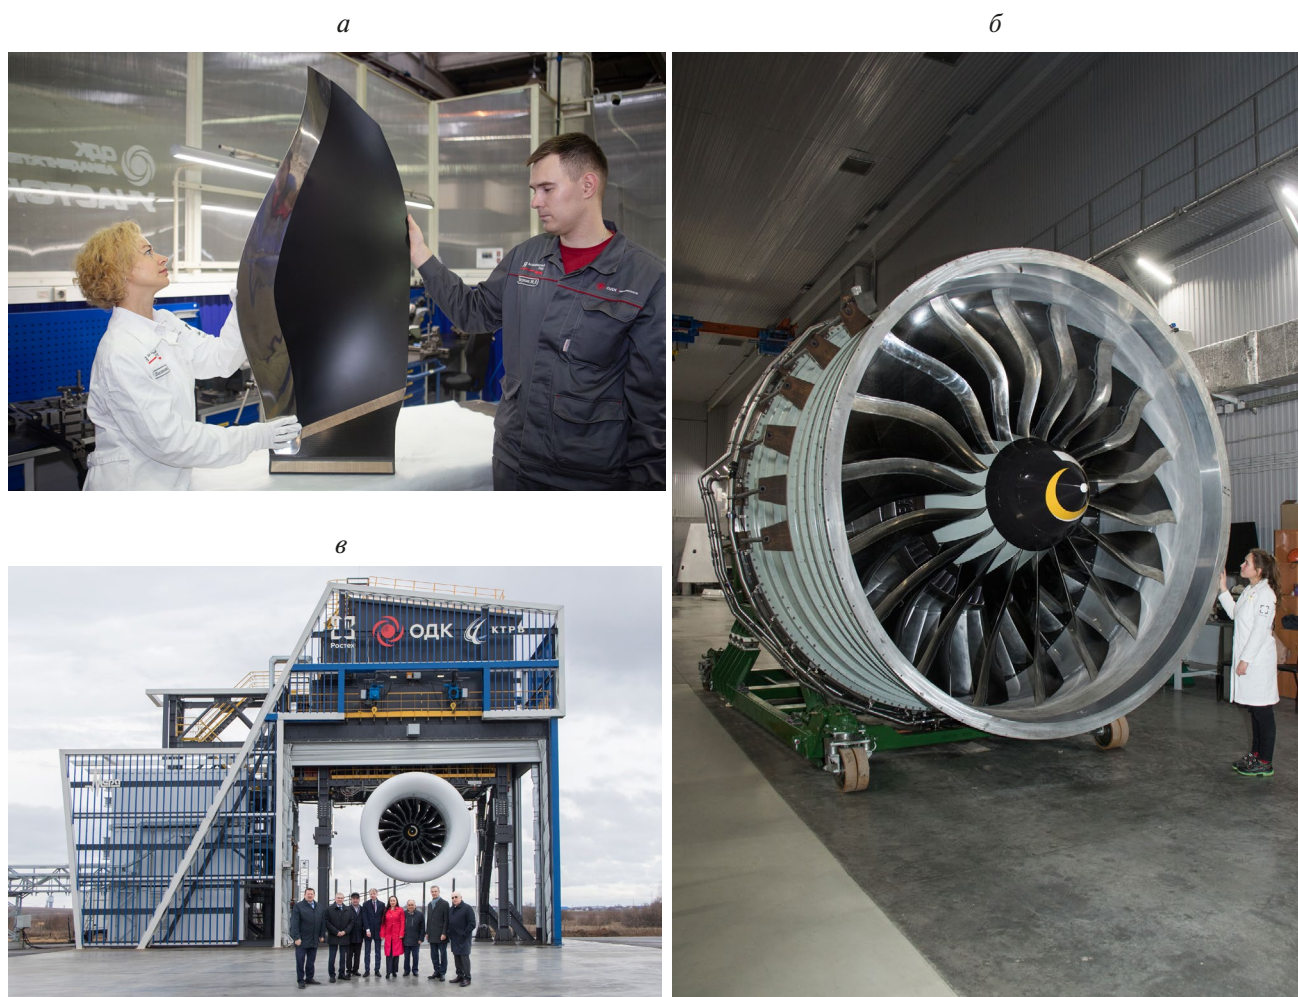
Сборка и подготовка к испытаниям двигателя-демонстратора технологий ПД-35:
